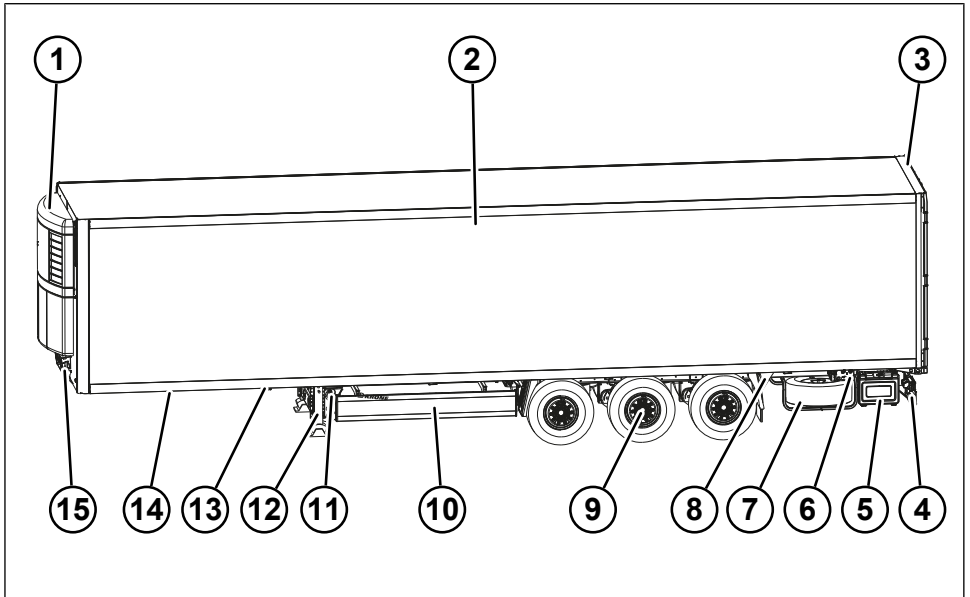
Übersicht Cool Liner (Beispiel)
